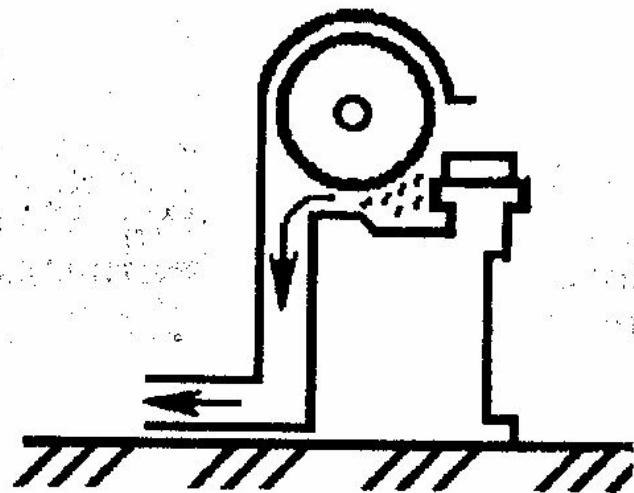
Схема вытяжной вентиляции заточного станка
